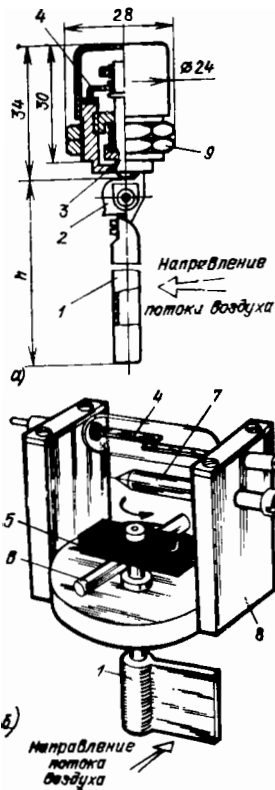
Конструкция простейшего сигнализатора потока воздуха: а — механического типа; б — магнитного типа; 1 — флажок; 2 — кулачок; 3 — шток; 4 — электроконтакты; 5 — постоянный магнит; 6 — упор; 7 — магнитный шунт; 8 — магнитопровод; 9 — гайки для крепления (показано положение, когда электроконтакты замкнуты)
